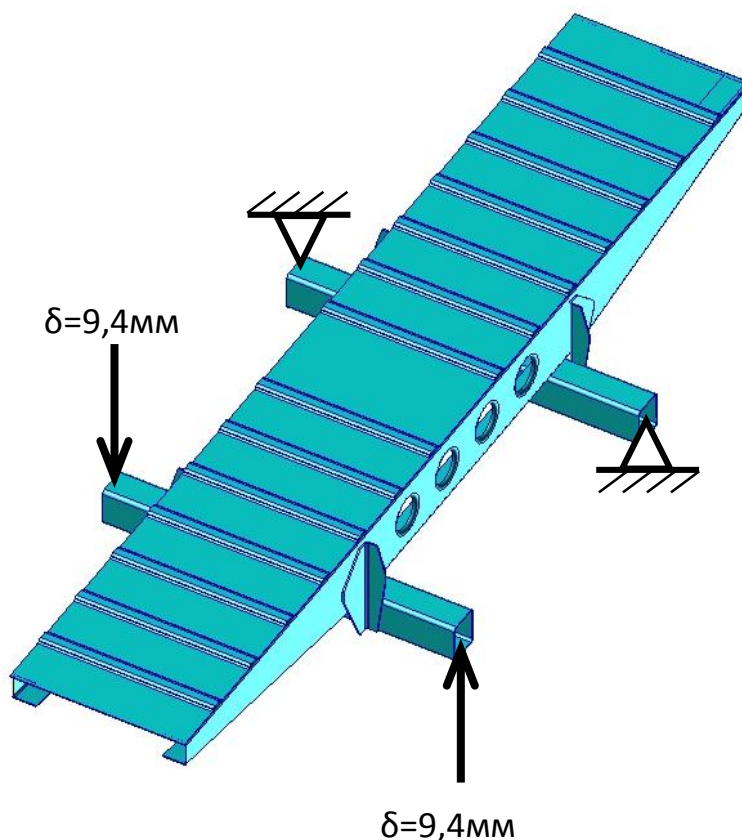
Схема нагружения на расчетный случай 2
